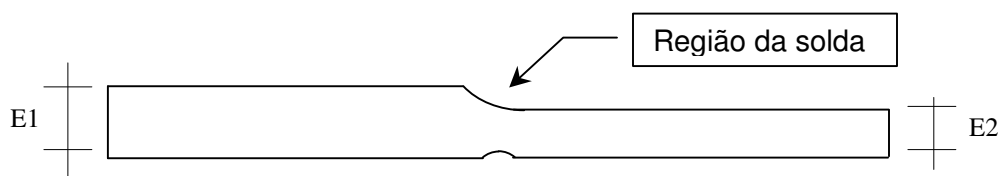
Blank soldado. União entre dois *blanks* de espessuras E1 e E2
